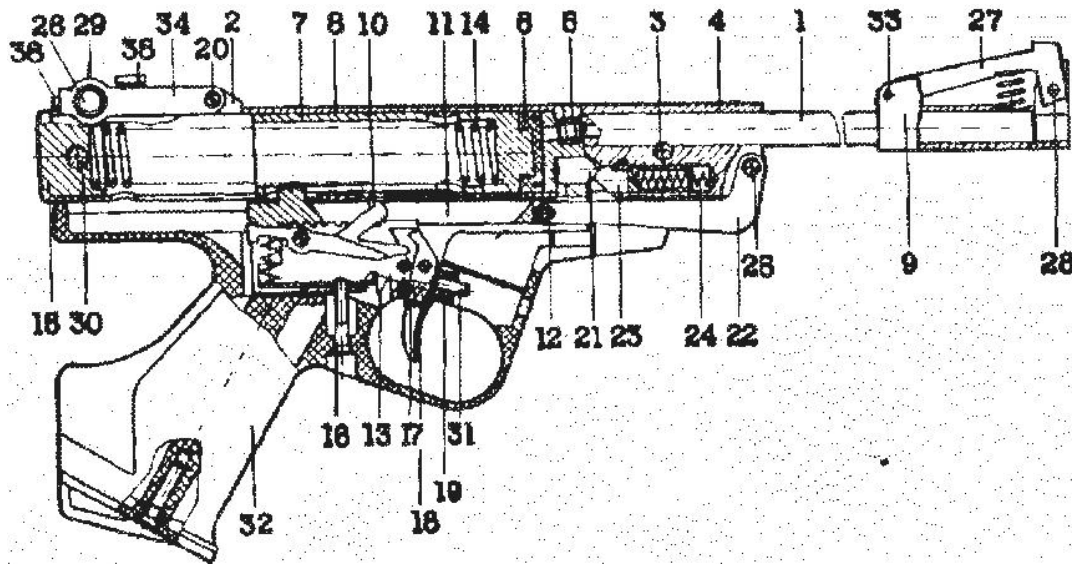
Устройство пневматического пистолета Иж-53 М:
